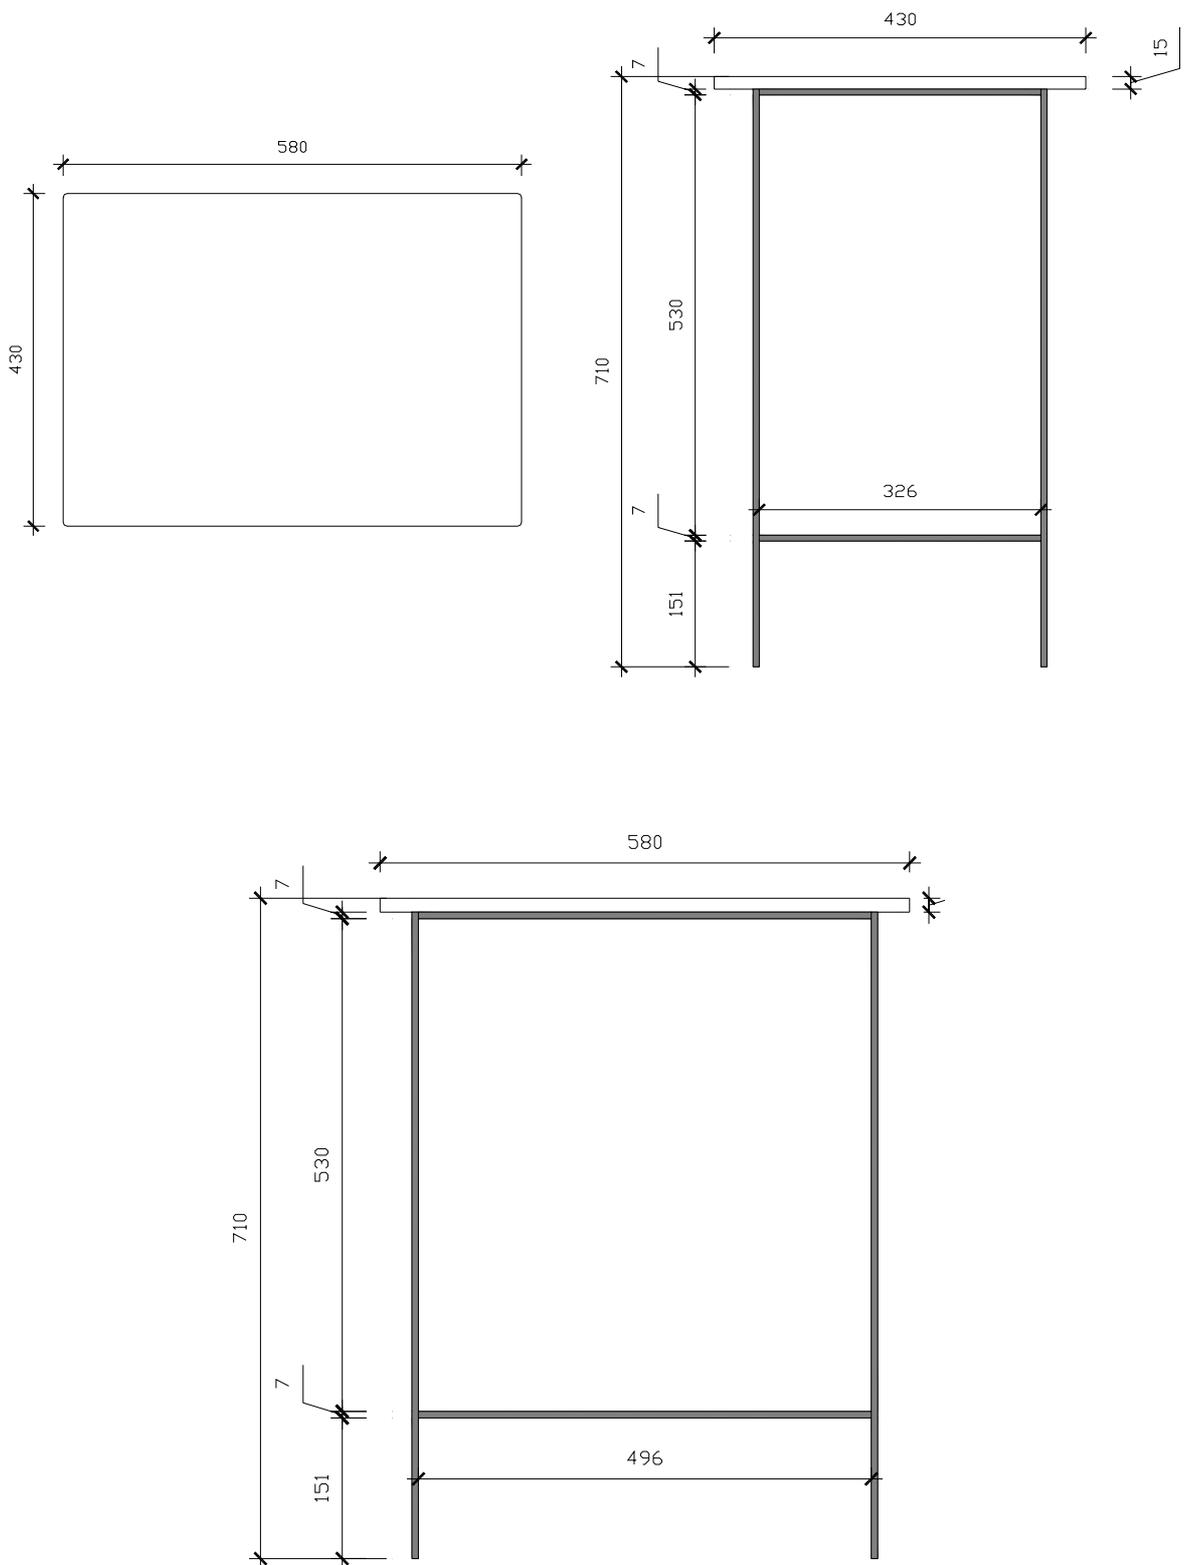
Mesa 4 - vistas superior, lateral e frontal.
